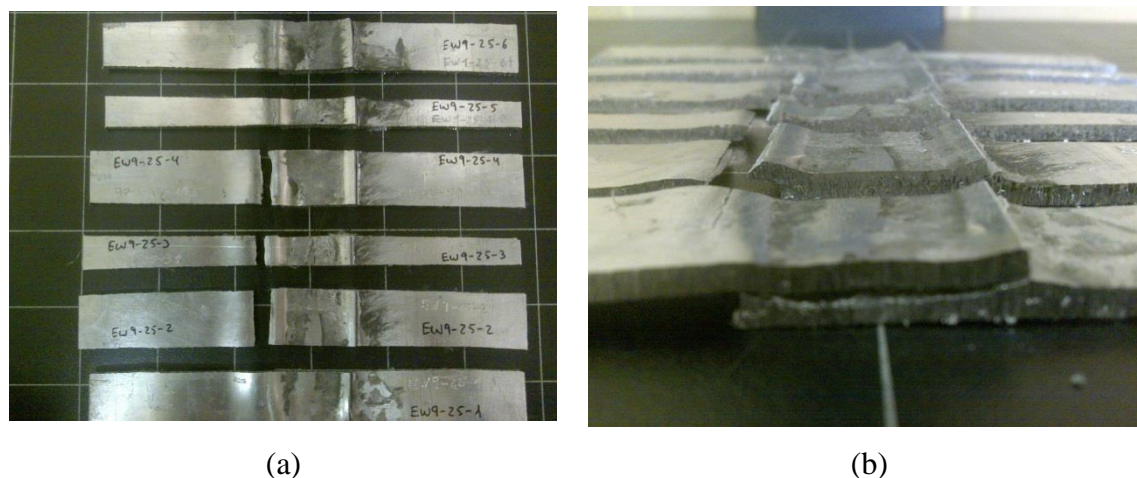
Soldadura EW8: (a) Vista geral; (b) Detalhe da zona soldada.
